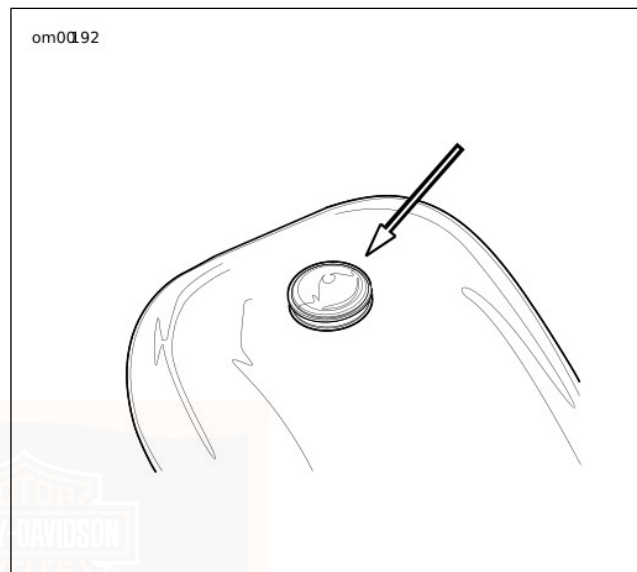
Bouchon de remplissage de carburant : modèles Sportster XL
